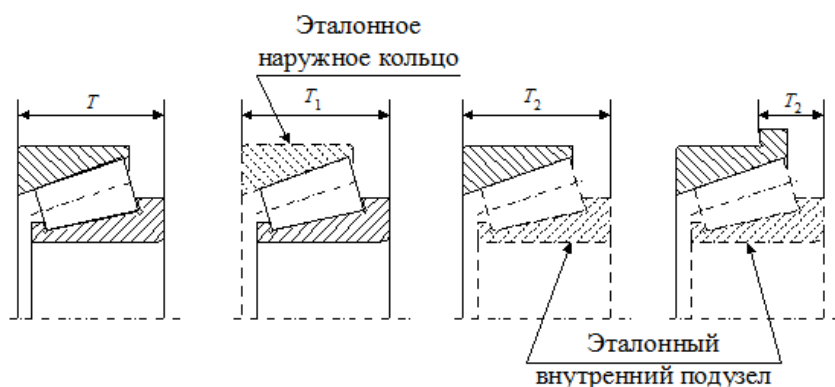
Дополнительные условные обозначения основных размеров роликовых конических подшипников
